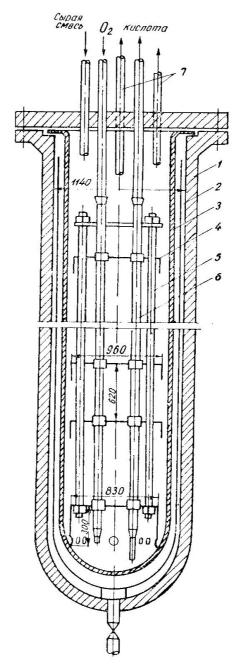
Автоклав для прямого синтеза азотной кислоты: 1 — корпус автоклава; 2 — защитный стакан; 3 — реакционный стакан; 4 — ситчатые тарелки; 5 — распорные штанги; 6 — чехольные трубы (каналы); 7 — переливные трубы.
